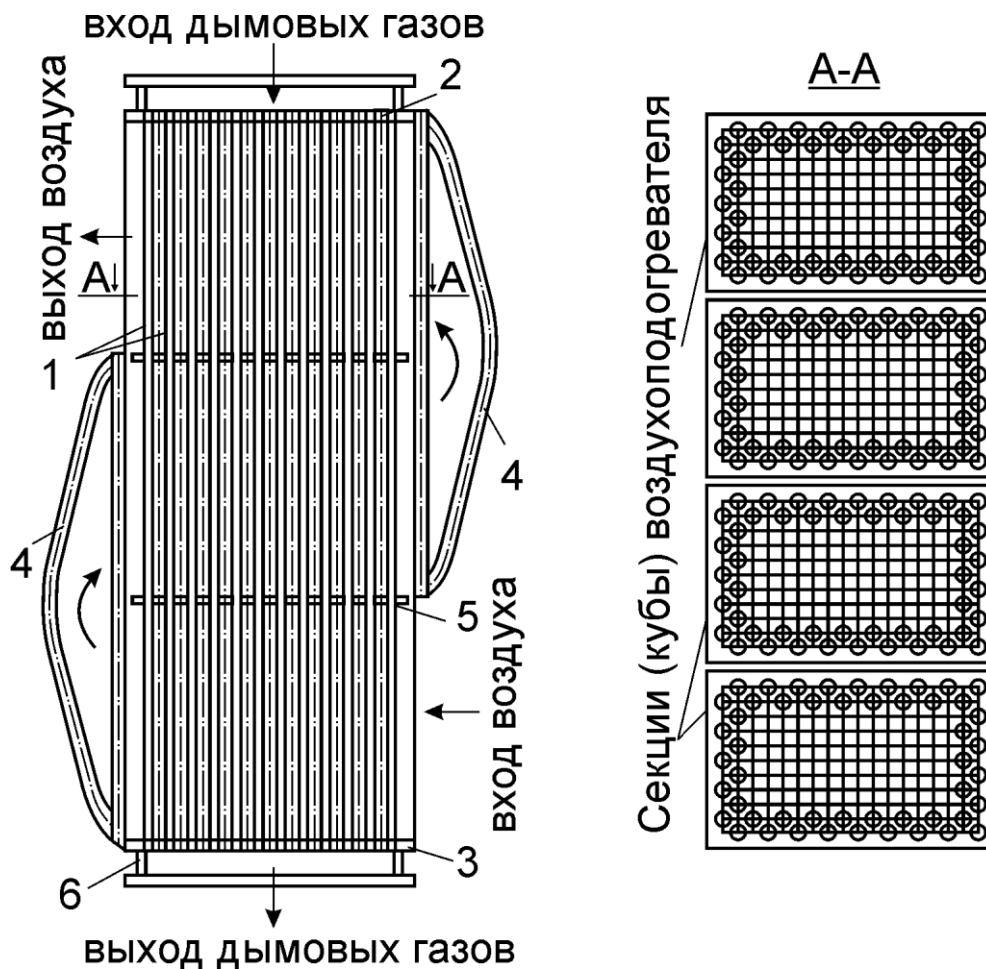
Трубчатый котельный воздухоподогреватель:
